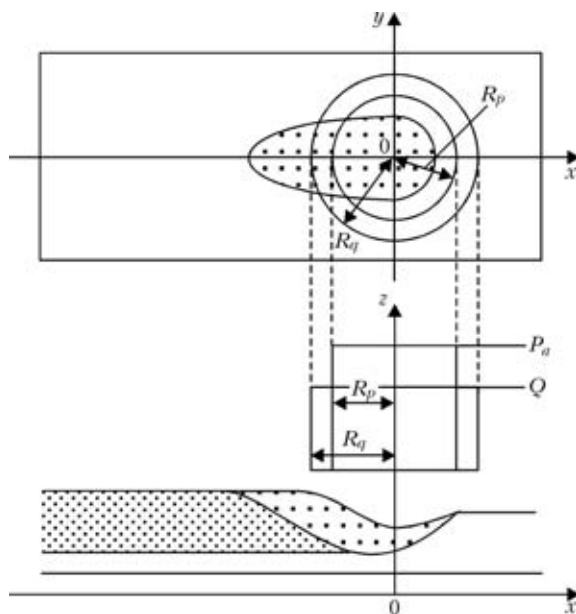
Схематическое изображение тепловложения и давления дуги на сварочную ванну (обозначения см. в тексте)
